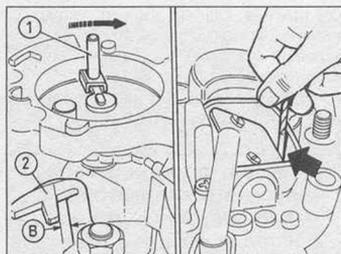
Проверка принудительного открытия воздушной заслонки (Глава 16)
